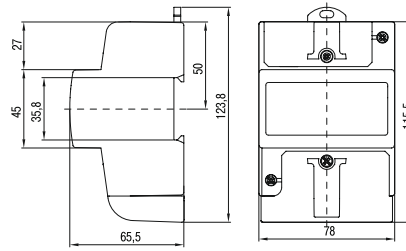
Габаритные и присоединительные размеры счётчиков габарита 1
